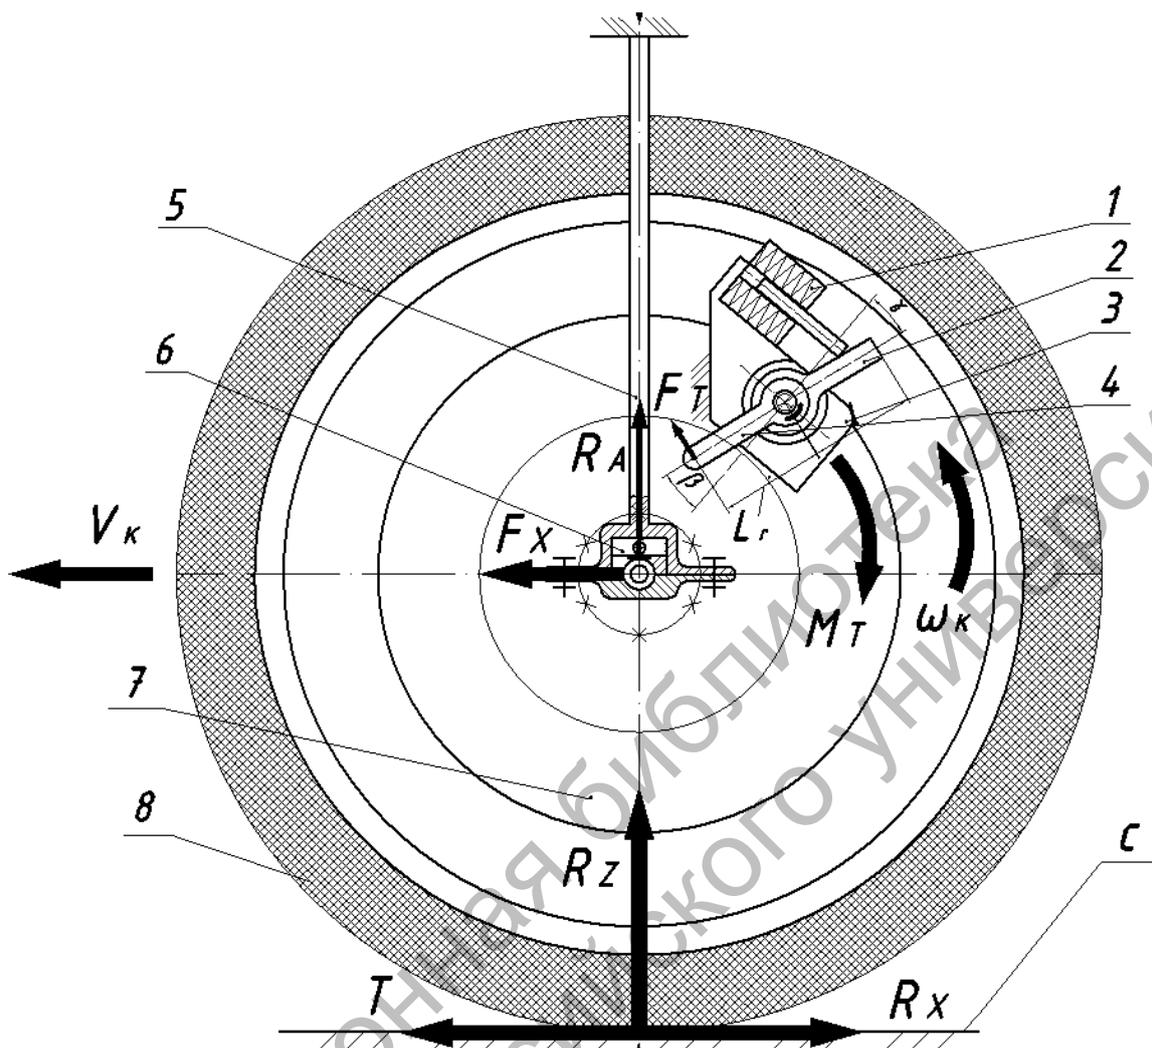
Способ измерения боковых сил в дисковом тормозном колесном механизме мотоцикла: 1 – исполнительный силовой элемент; 2 – скоба тормозная; 3 – корпус; 4 – рычаг; 5 – труба передней вилки; 6 – датчик боковых сил; 7 – диск тормозной; 8 – колесо; R_X – продольная реакция; R_Z – нормальная реакция; C – опорная поверхность; T – тормозная сила; F_X – толкающая сила корпуса мотоцикла; M_T – тормозной момент; ω – угловая скорость колеса; V_K – поступательная скорость колеса; R_A – реакция в опорном устройстве; F_T – сила, приложенная к рычагу тормоза
